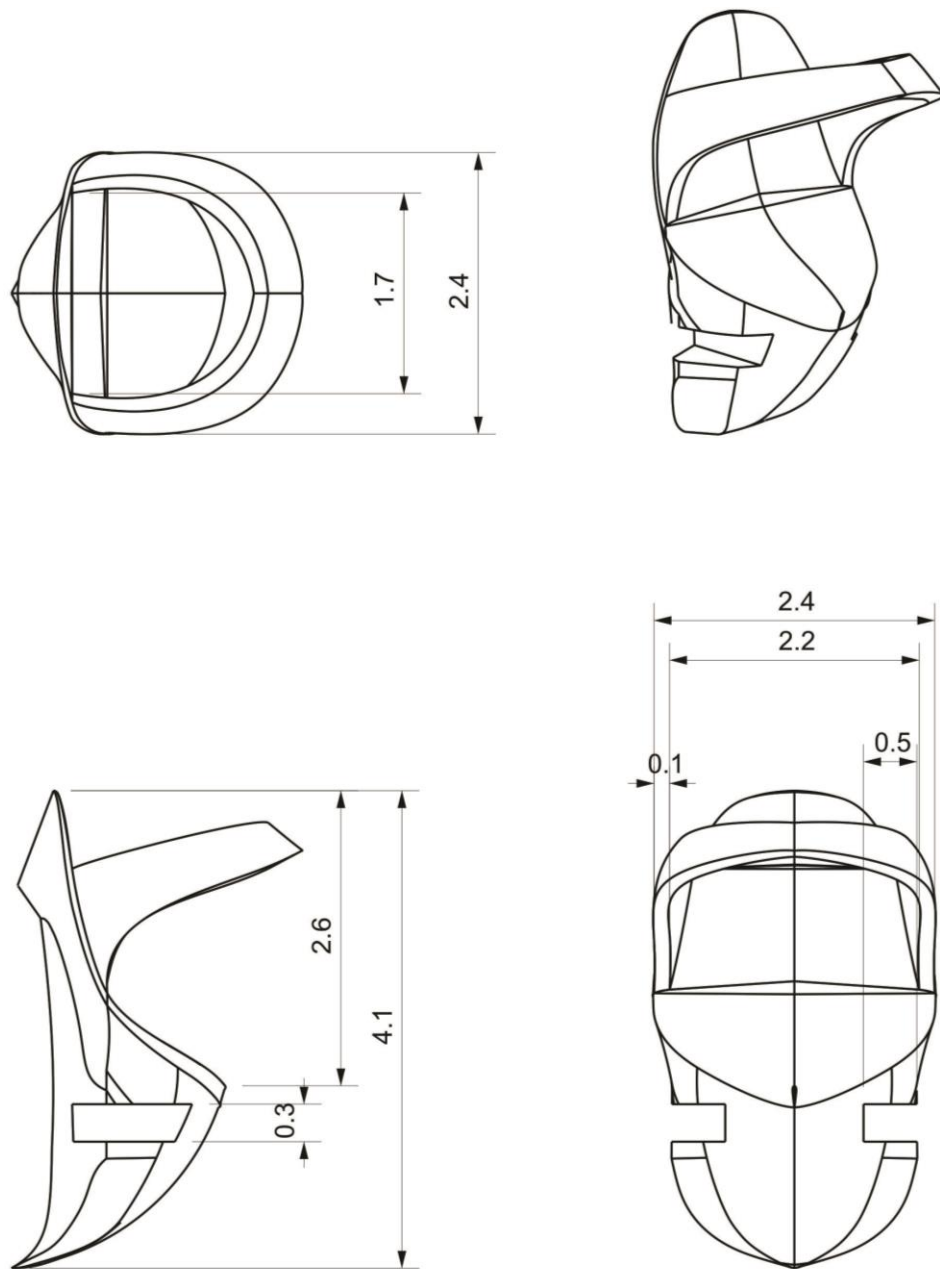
Planos pieza #1 (Dimensiones en cm)
